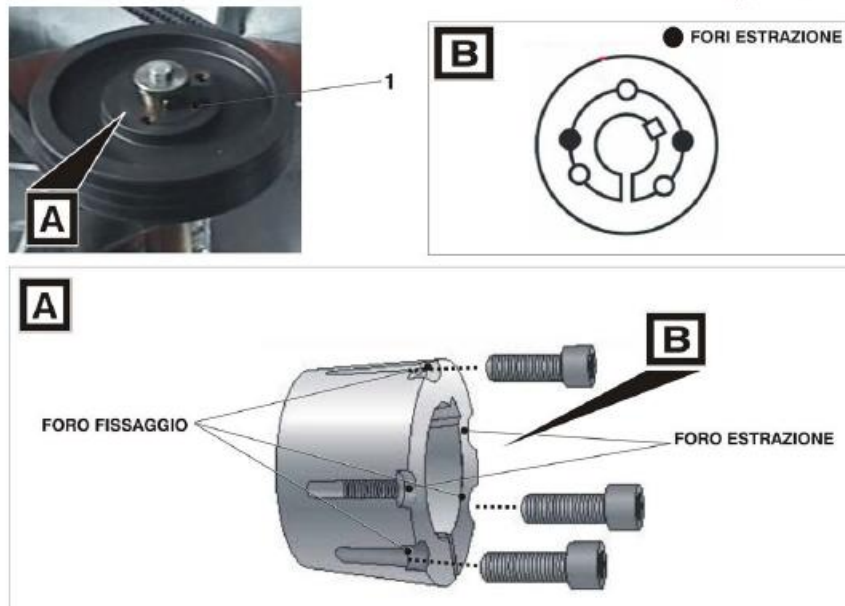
Detail der kegelförmigen Befestigungsbuchsen mit Angabe der Bolzenlagerungen.
